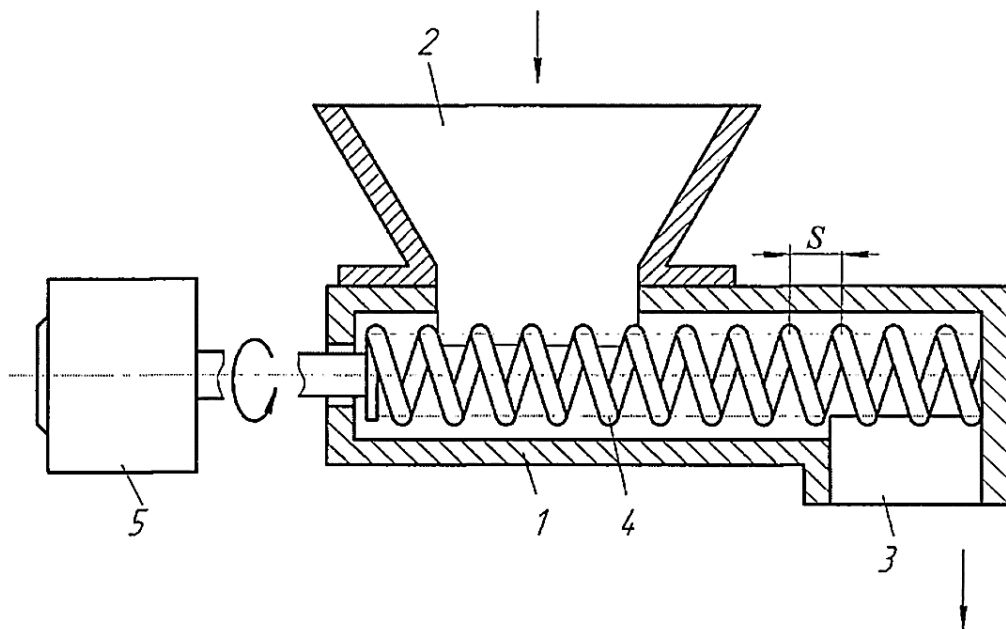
Конструктивно-технологічна схема експериментального дозатора: 1 - циліндричний кожух; 2 - завантажувальний бункер; 3 - вивантажувальна горловина; 4 - гвинтова спіраль; 5 -привід
